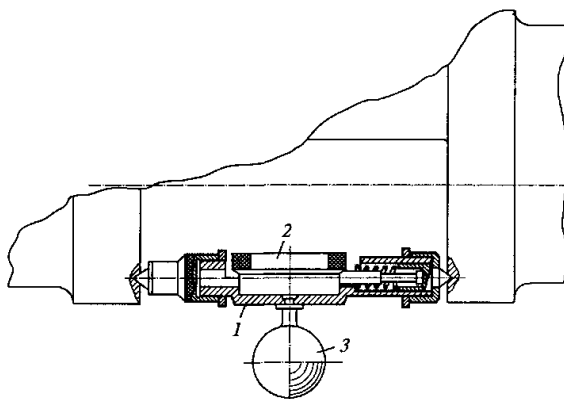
Индикаторное приспособление для измерения расхождения щек шатунной шейки коленчатого вала дизеля:
